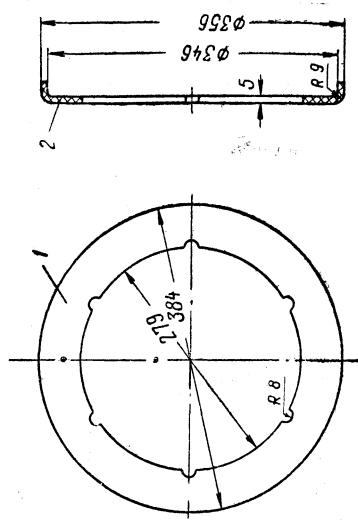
Воротник тормозного цилиндра (кожаный): 1 — заготовка; 2 — отштампованный
